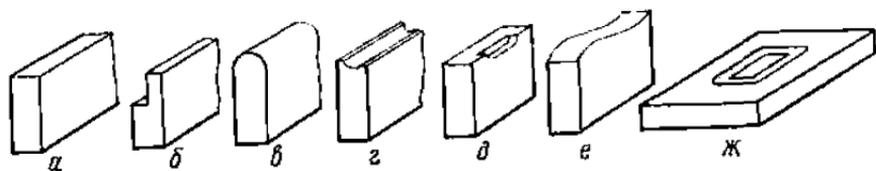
Некоторые виды профилей при обработке на фрезерных станках
